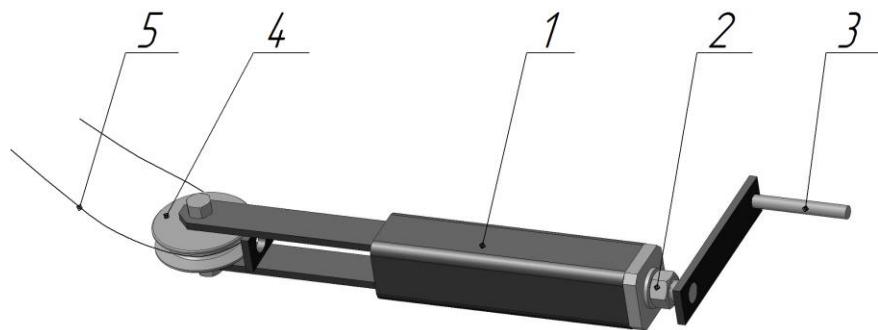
Общий вид натяжного устройства (корпуса) стояночного тормоза
